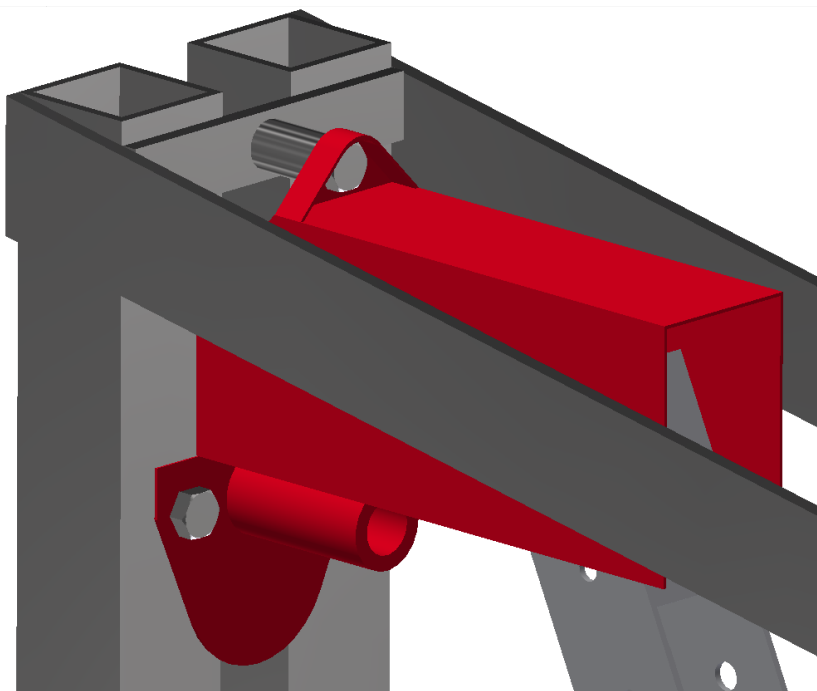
Uchycení pneumatického aktuátoru - pohled 1
